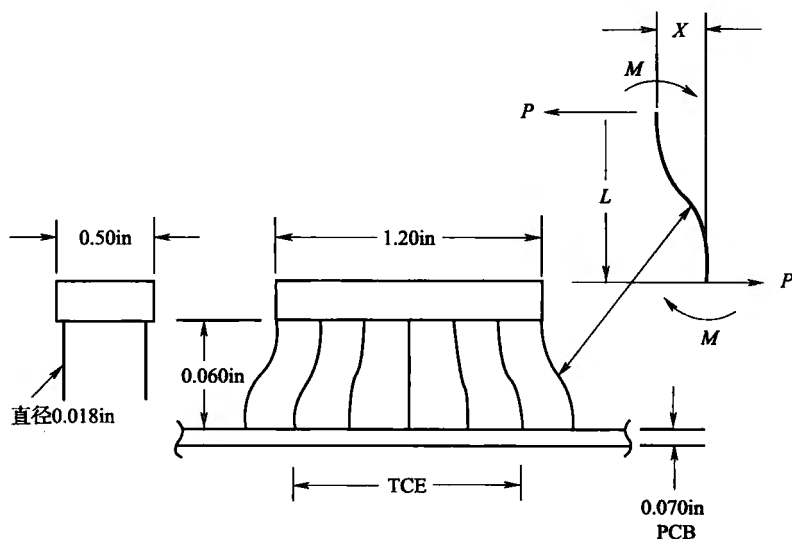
PCB 与器件热胀系数 (TCE) 之差将使热循环环境中的引线弯曲
